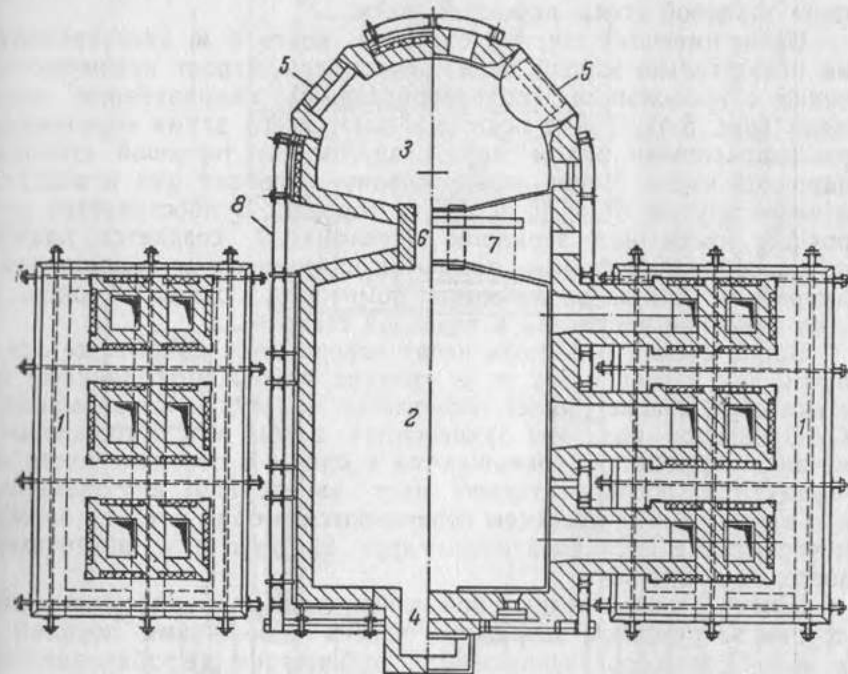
Ванная печь с поперечным ходом пламени для механизированной выработки колб.
